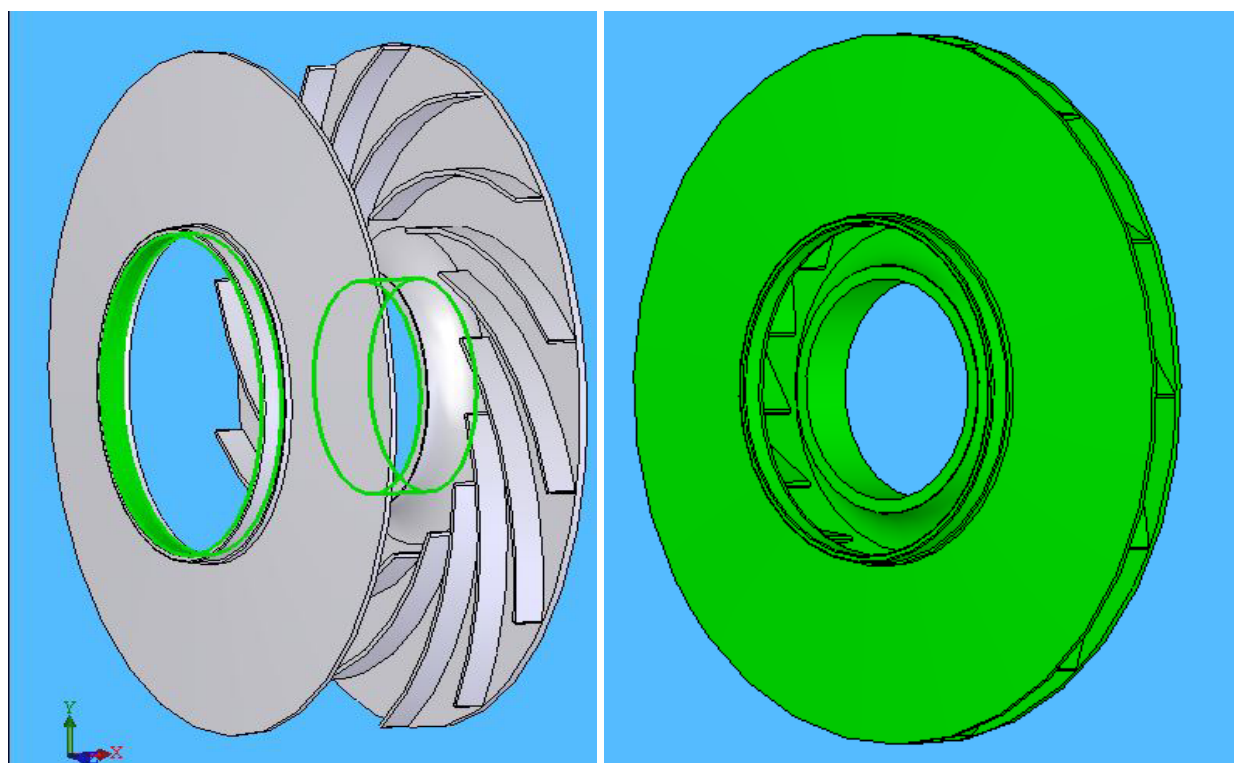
3D-модель рабочего колеса с радиальными лопатками
